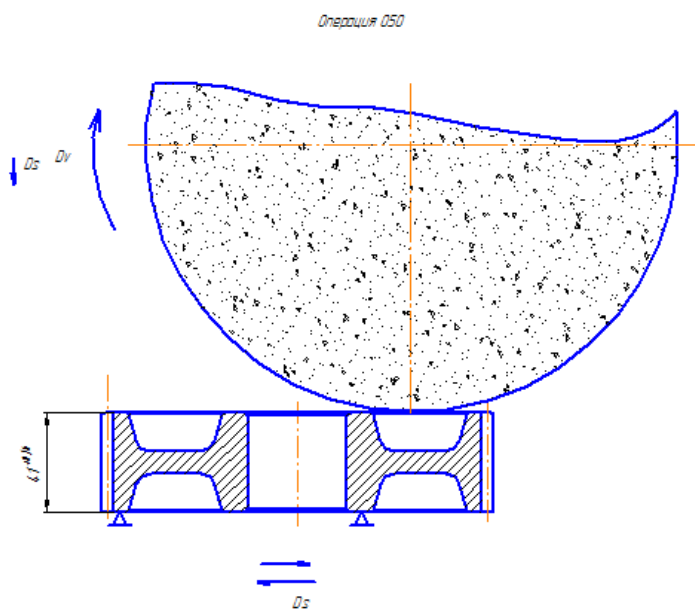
Процесс шлифования торца зубчатого колеса
